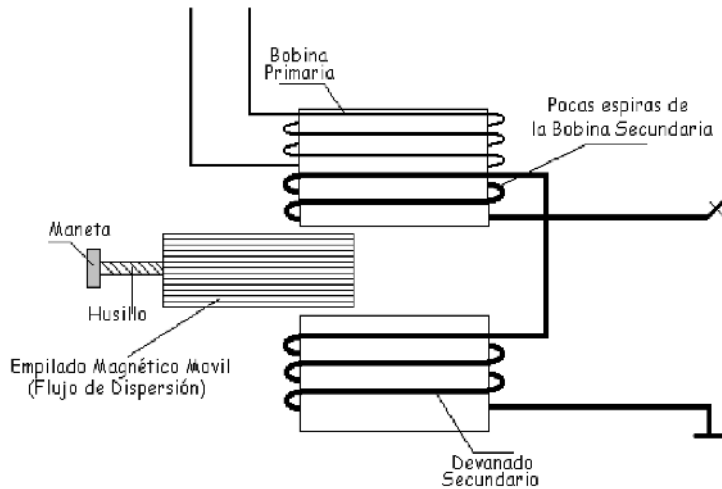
Disposición de los devanados en un equipo para obtener más intensidad de soldadura.
